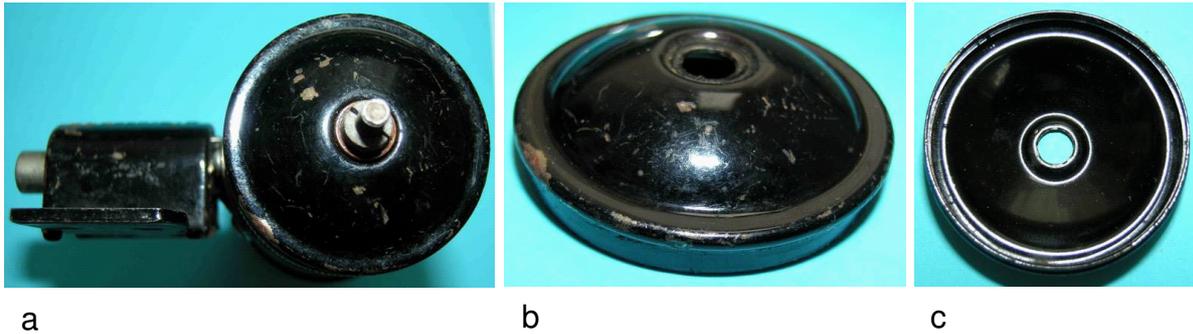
Boden: a) Bodenansicht des Dynamos, b) Seitenansicht, c) Innenansicht
